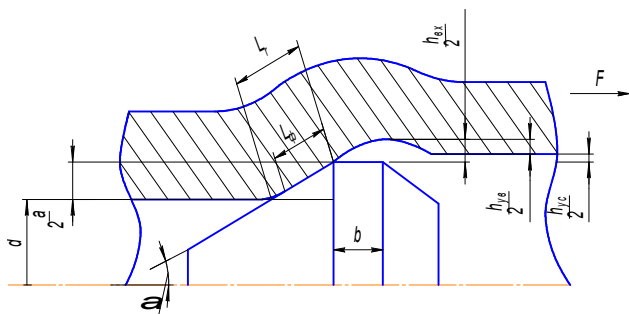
Схема взаимодействия инструмента-дорна с цилиндрической заготовкой при $D/d < 3$
